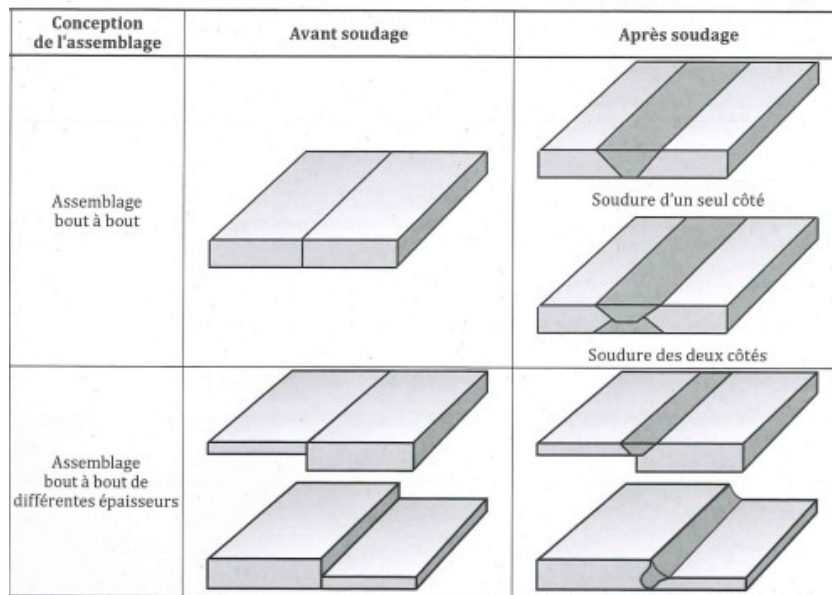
Types de joints soudés bout à bout [20]
